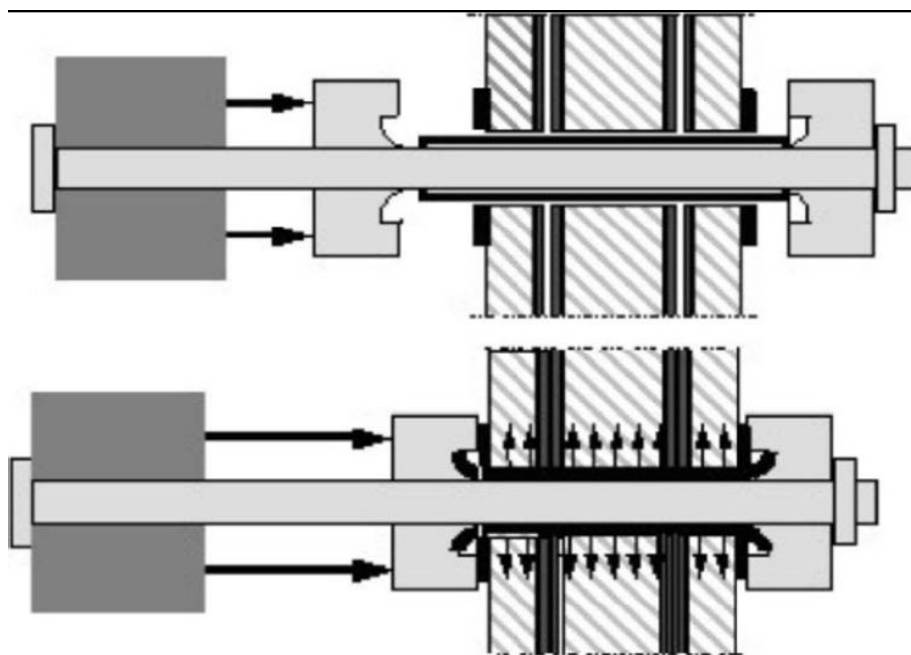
tecnica di inserimento del connettore a tubo
